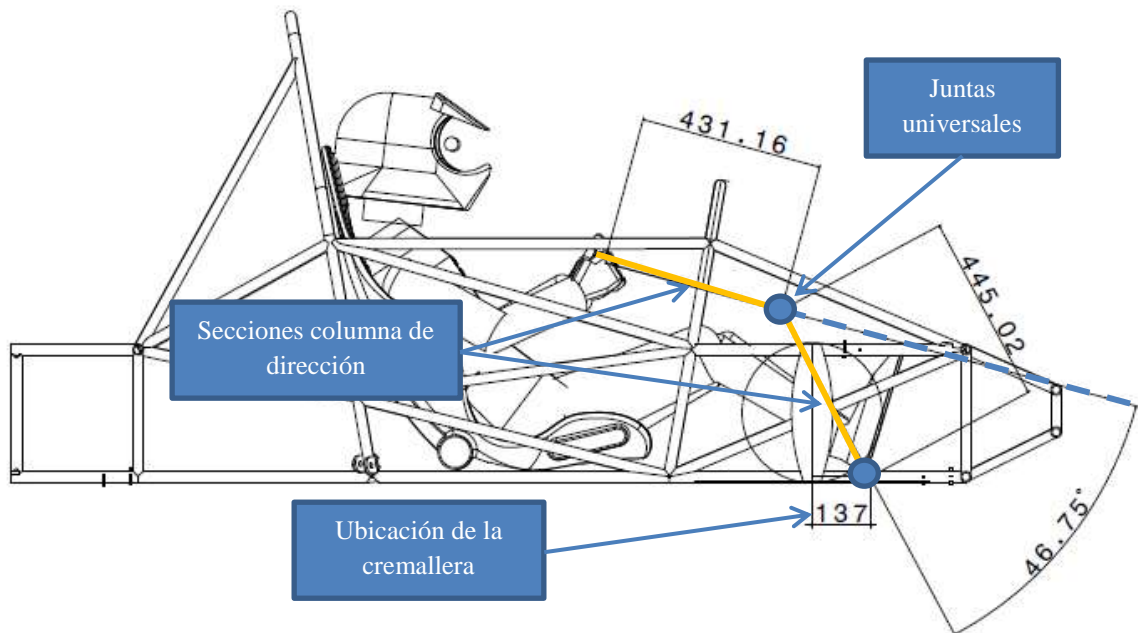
Geometría de la columna de dirección. (Elaboración propia)
